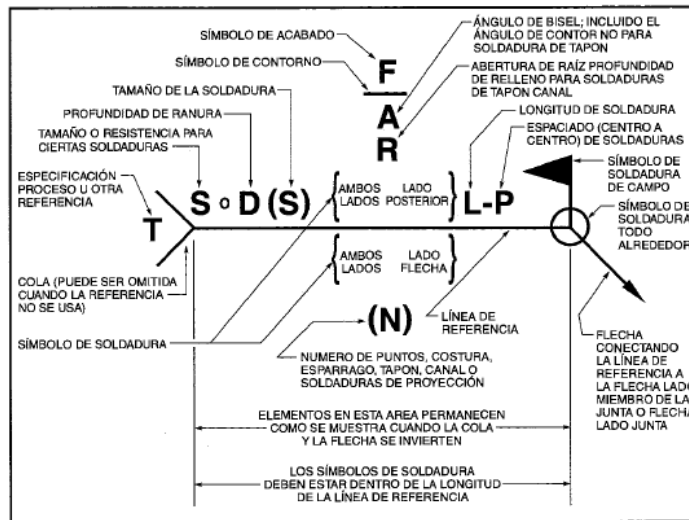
Estándar de elementos de un símbolo de soldadura. (AWS) [15]
